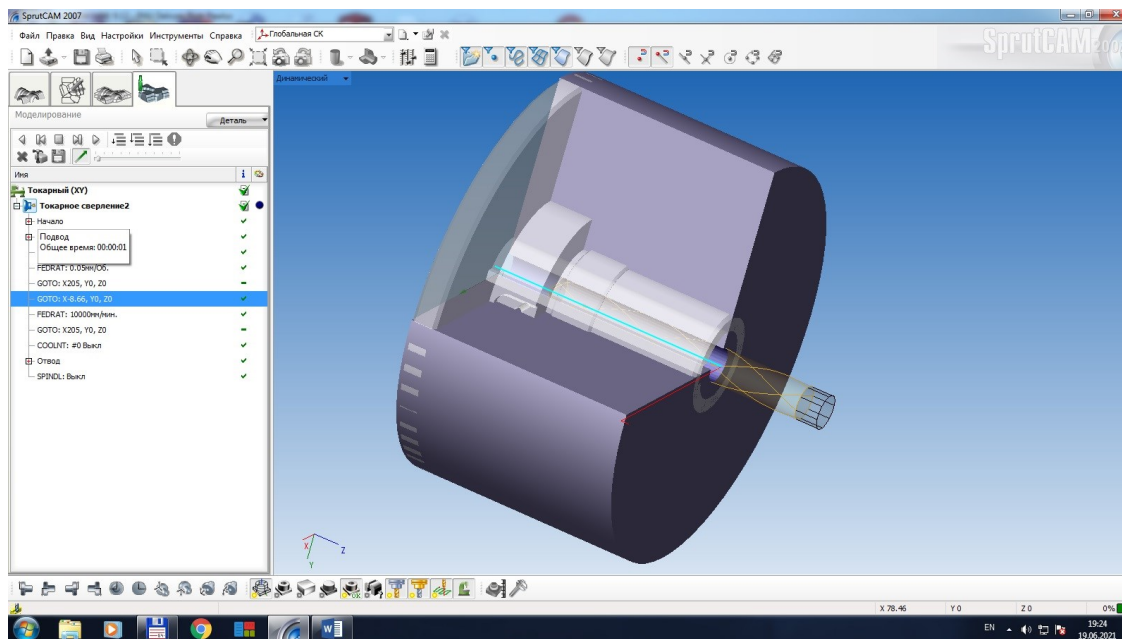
Інструмент та заготовка в процесі обробки.
